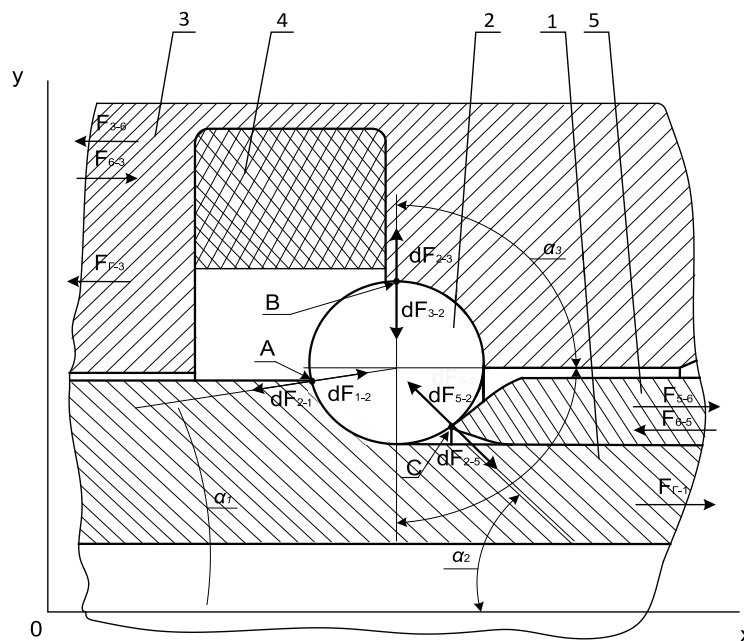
Схема нагружения соединения труб на I этапе демонтажа:
